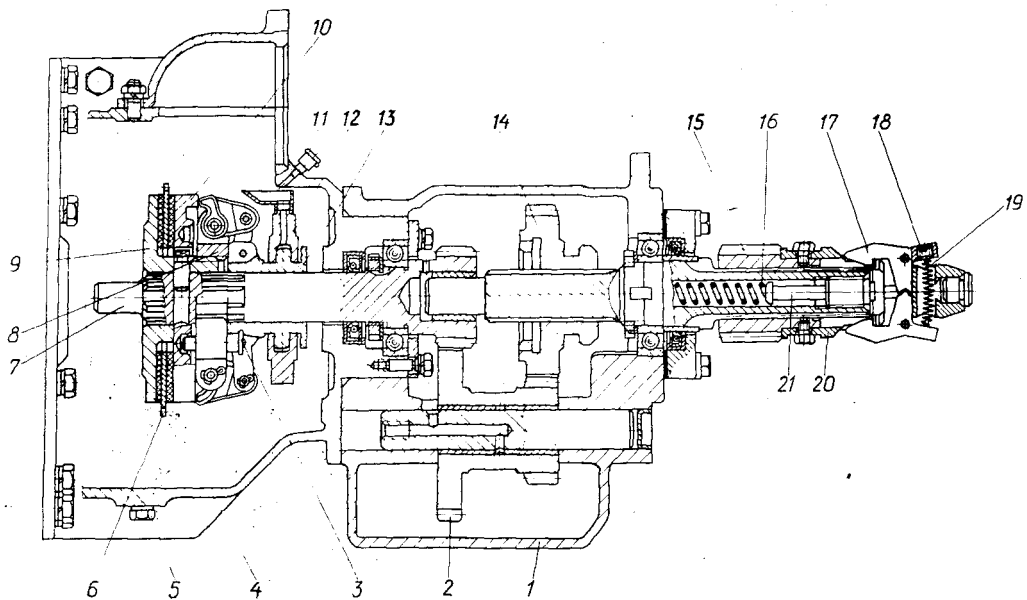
Муфта сцепления и редуктор с муфтой механизма включения:
